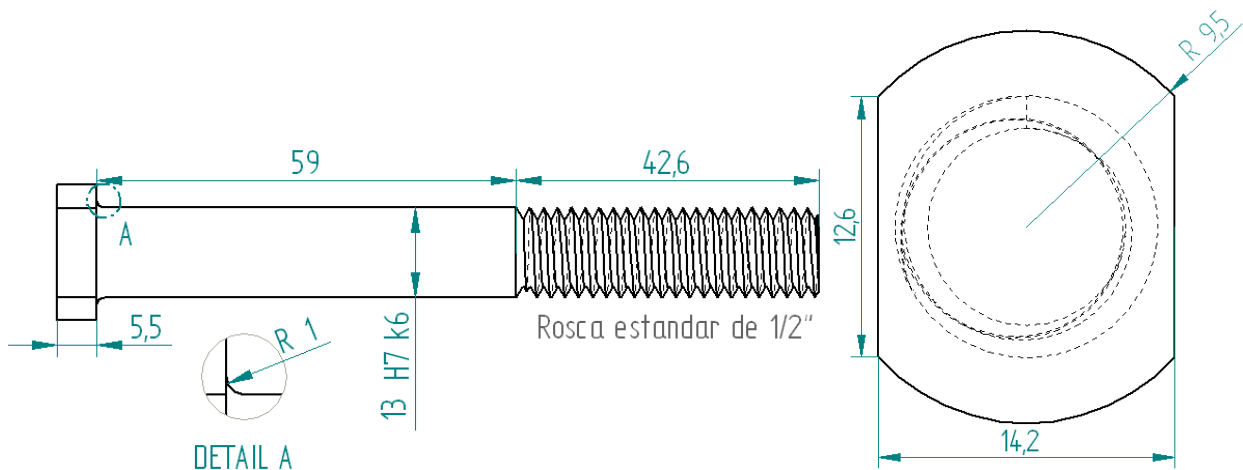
Vista lateral y frontal del eje de rodamientos con acotaciones en milímetros.
